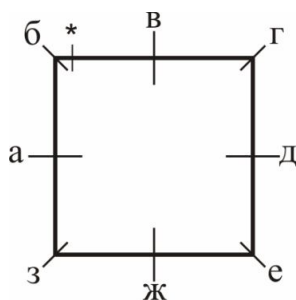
Схема последовательности измерений толщины корочки заготовки
